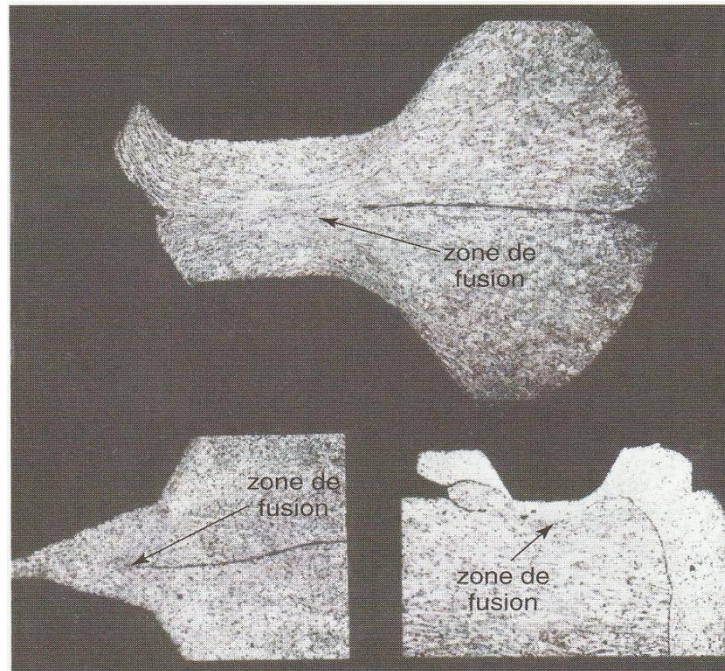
Exemples de pièces soudées à froid. Les deux parties sont de l'aluminium (1003). Notez la forte indentation de la surface.
